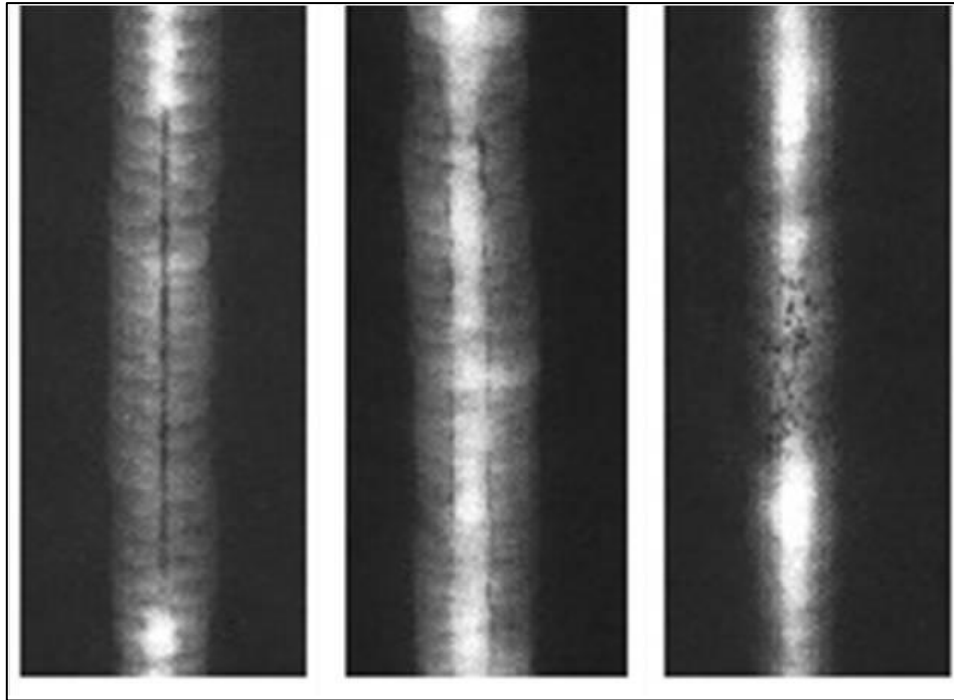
Placas radiográficas de cordones de soldadura, cada una con indicaciones
